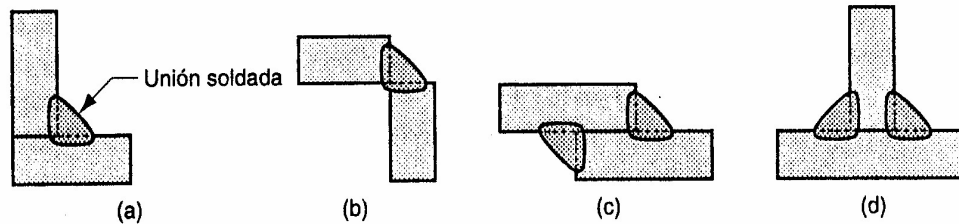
Diversas formas de soldadura de filete: a) unión de esquina con filete interno único, b) unión de esquina con filete externo único, c) unión sobrepuesta con filete doble, y d) unión en T con filete doble. Las líneas con guiones muestran los bordes originales de las placas.
